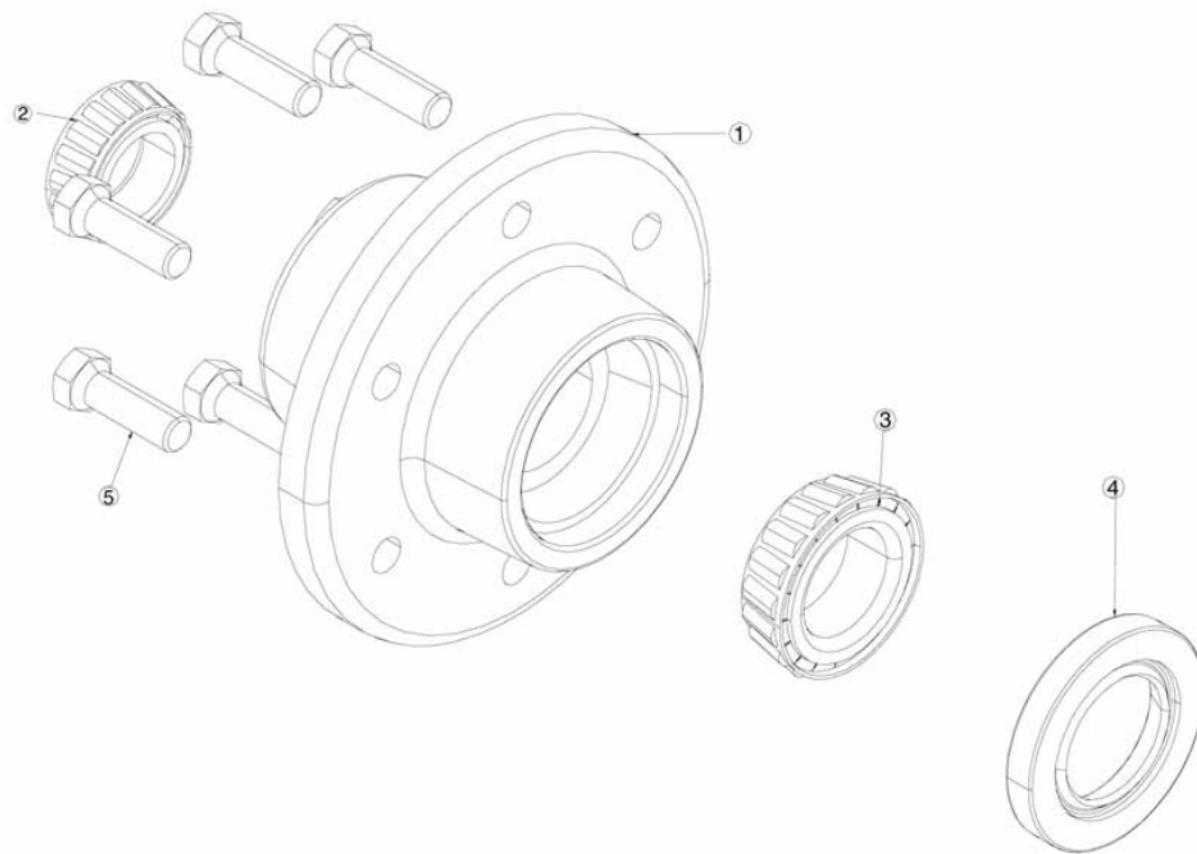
Чертеж сборки ступицы - С2339-00
